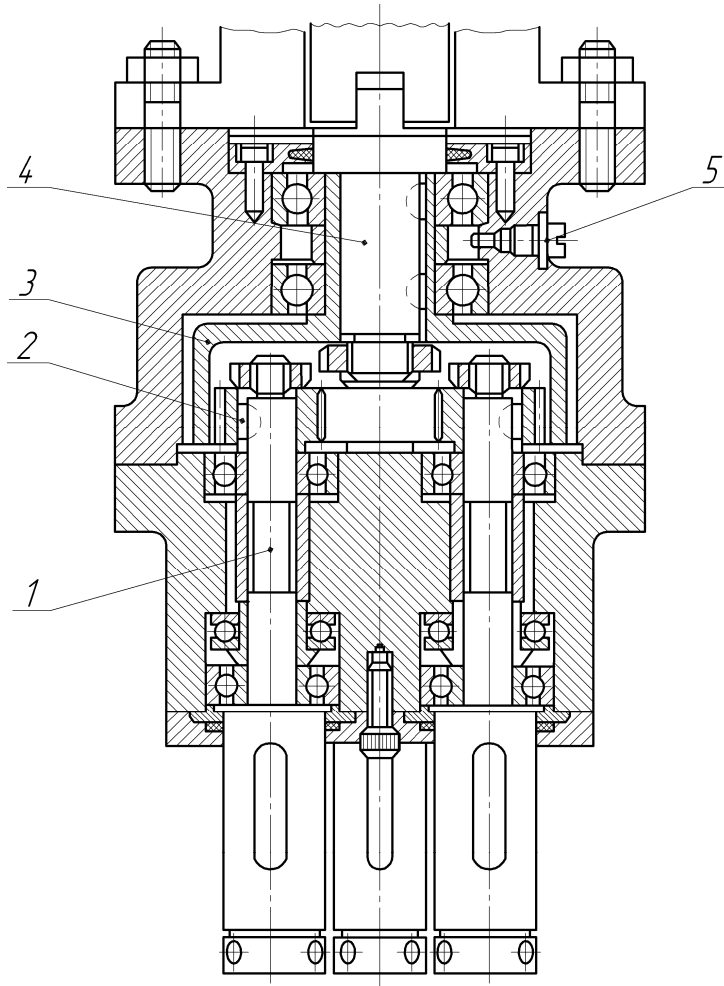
Будова багатошпindelної головки з консольним розташуванням зубчастих коліс:
